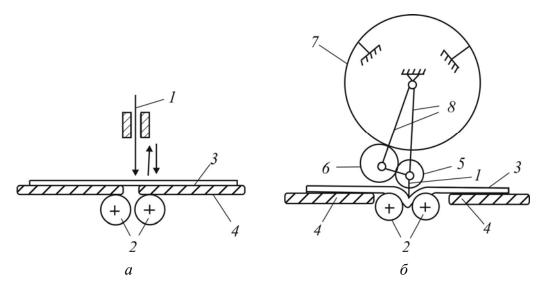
Ножевые устройства для фальцевания тетрадей и листов: a-c возвратно-поступательным движением ножа; $\delta-c$ планетарным механизмом ножа: l- нож; 2- валики; 3- лист; 4- стол; 5- приводное колесо; 6- шестерня; 7- неподвижное колесо; 8- водило
